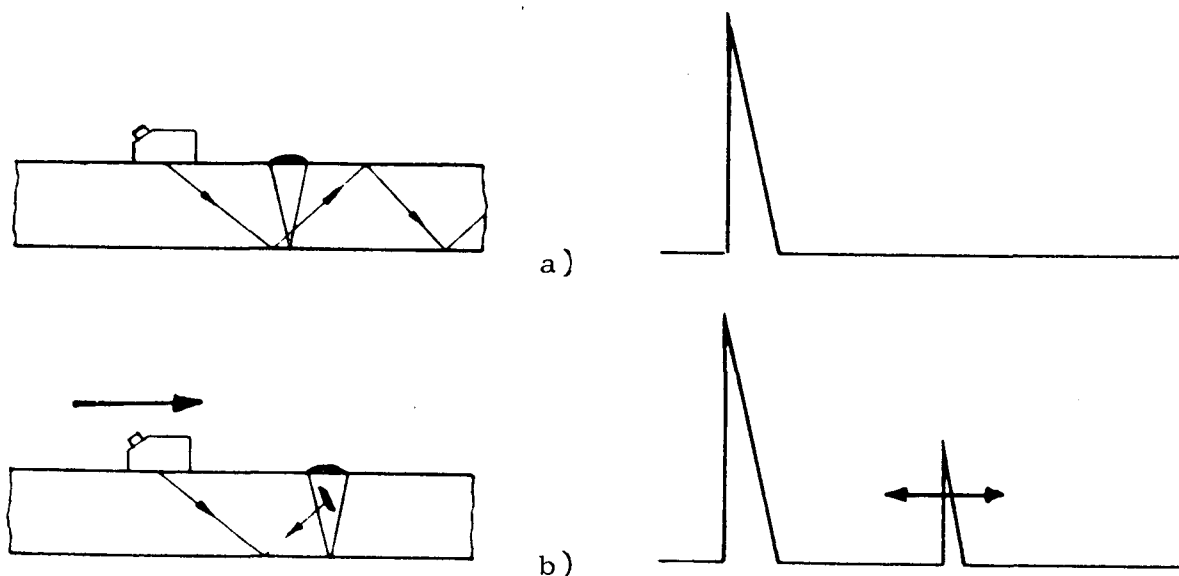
Ensayo de soldaduras por reflexión
